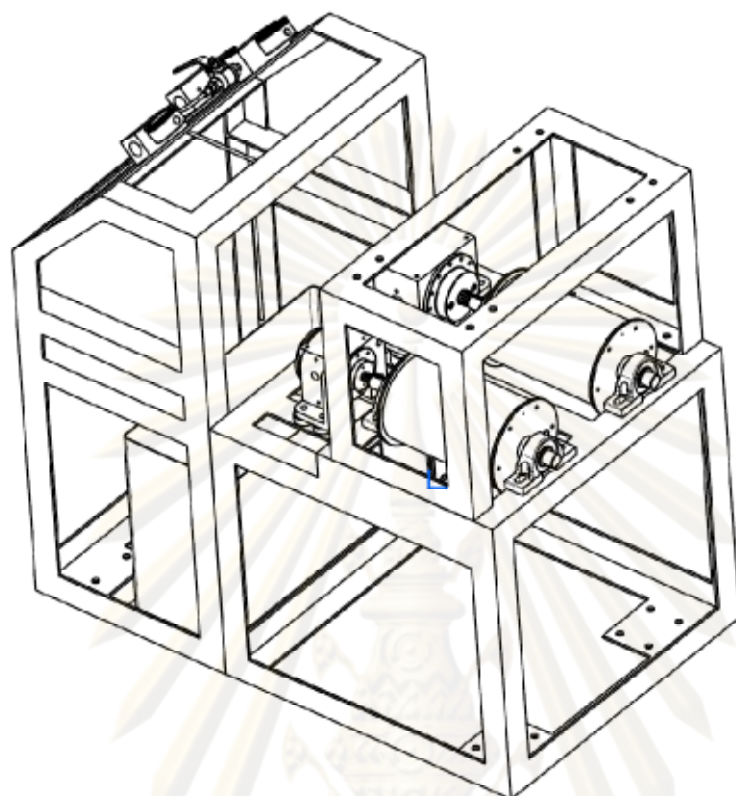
แบบ Drawing ของ Prony tube 2
